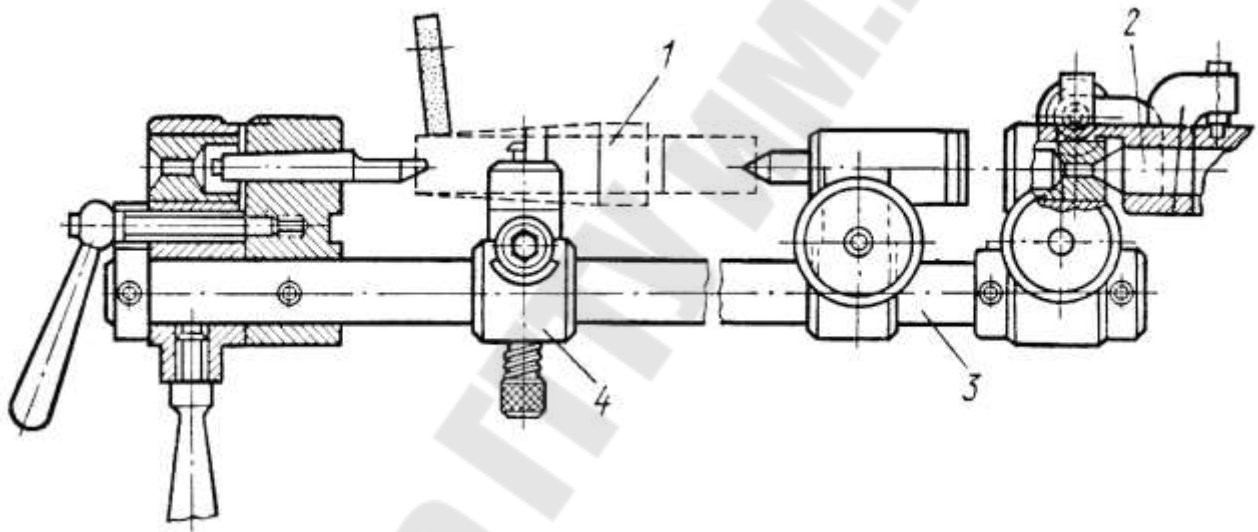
Делительное приспособление для конической заточки задней поверхности режущей части метчика: 1 – метчик; 2 – центр станка; 3 – штанга; 4 – упорка
